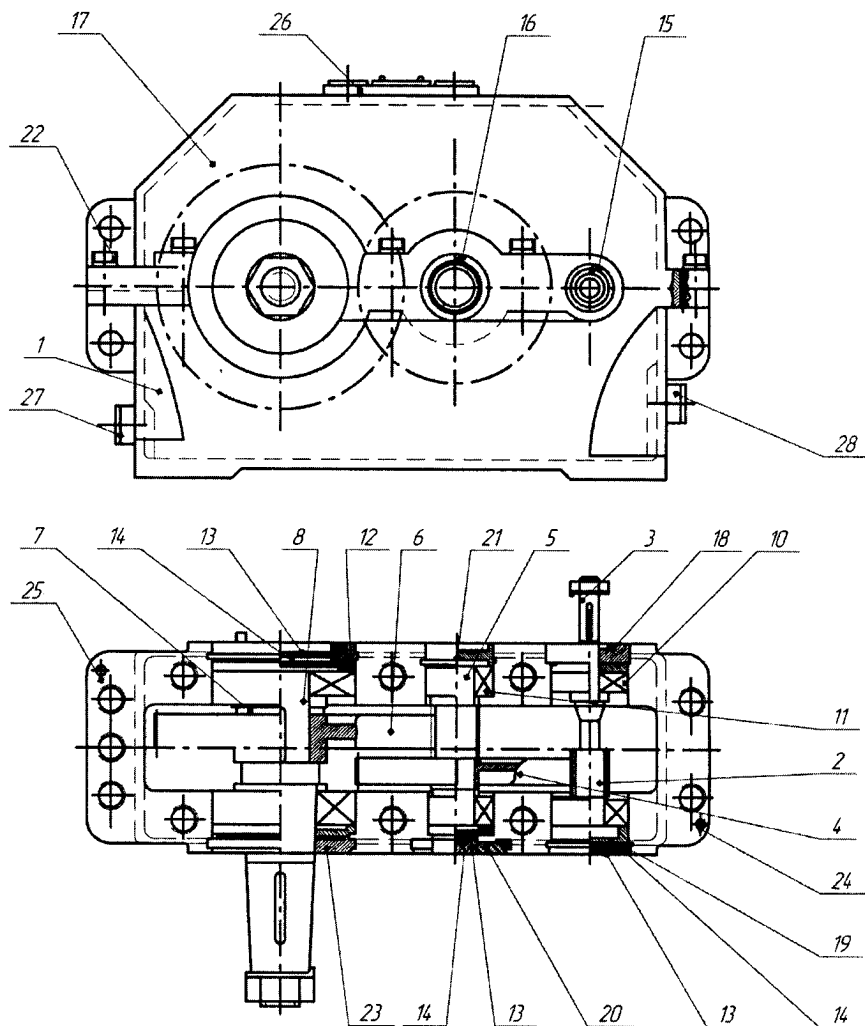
Конструкція двоступінчастого редуктора Ц2У-160
